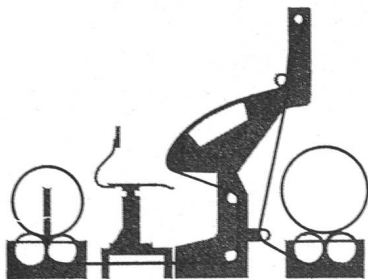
Vorschaumaschine P 6 (Maschinenbau Mengen)
